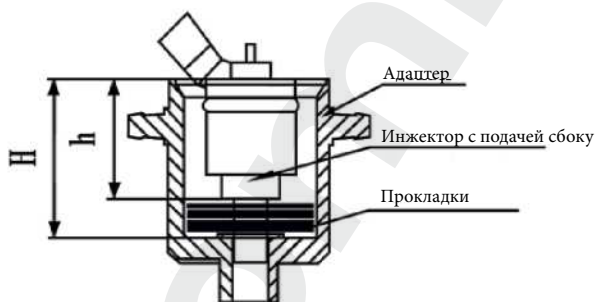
Схема установки держателя инжектора с боковой подачей топлива
